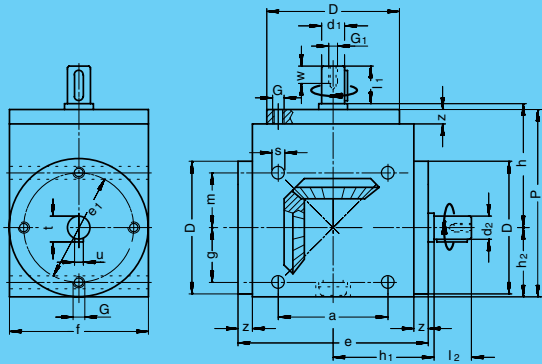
Ausführung ohne Gewichtserleichterung, rechts/rechts drehend
